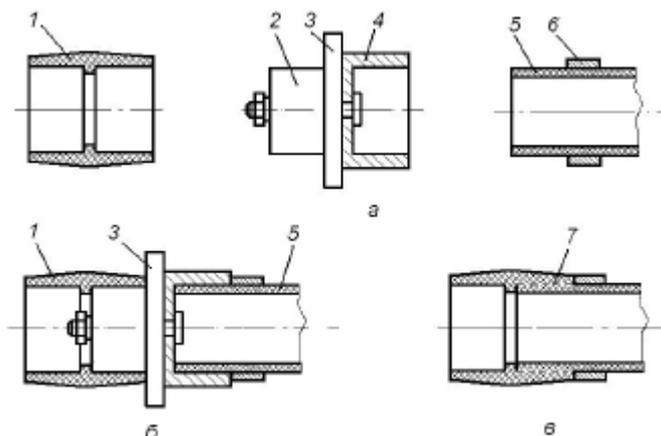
Схема сварки внахлест: а – нагреватель и стыкуемые детали; б – нагрев свариваемых поверхностей; в – сварное соединение трубы с муфтой; 1 – соединительный элемент; 2 – дорн; 3 – нагреватель; 4 – гильза; 5 – труба; 6 – ограничительный хомут; 7 – сварной шов
